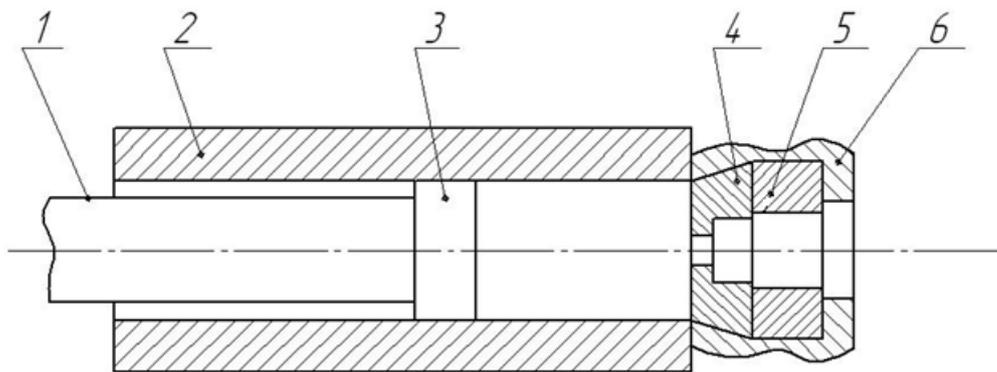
Схема сборки прессового инструмента для прессования профилей сплошного сечения прямым методом: 1–пресс-штемпель; 2–внутренняя втулка контейнера; 3–пресс-шайба; 4–матрица; 5–подкладка; 6–матрицедержатель.
